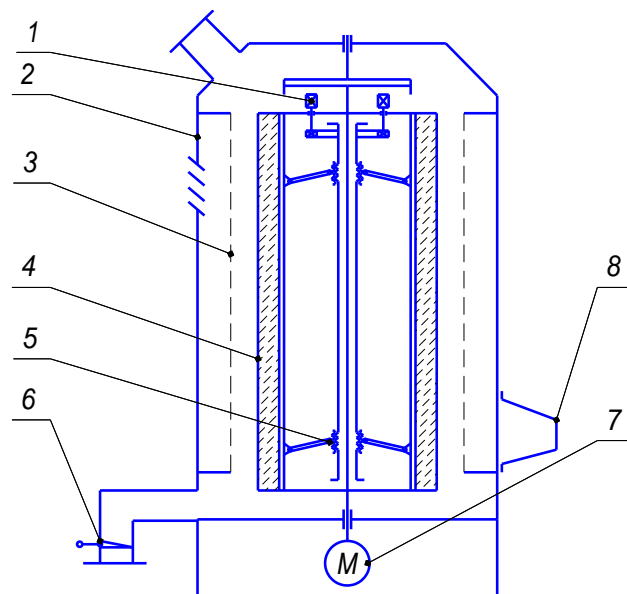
Машина роторно-брусова 1,6-регулятори; 2-корпус; 3-сітка; 4-брус; 5-важільно-гвинтовий механізм; 7-привід; 8-патрубок повітряний; 9-диск захисний.
